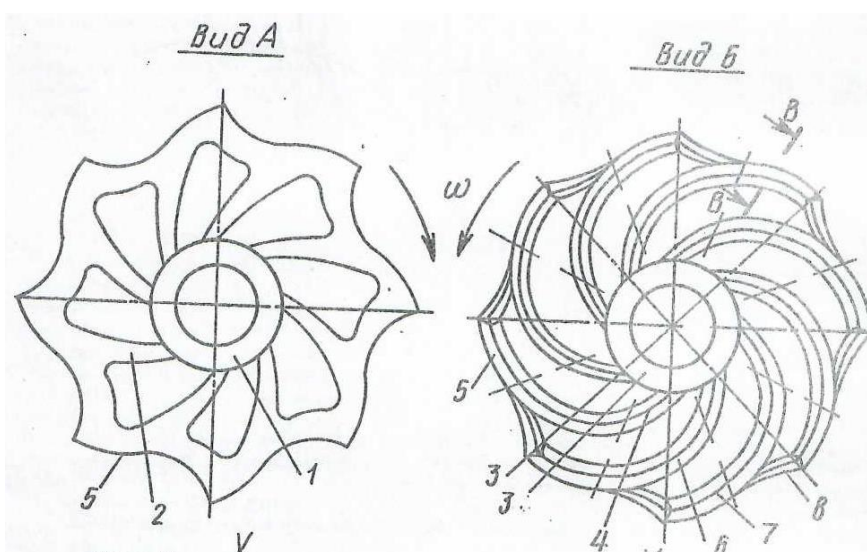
Вид А і вид Б на рис 2.5
